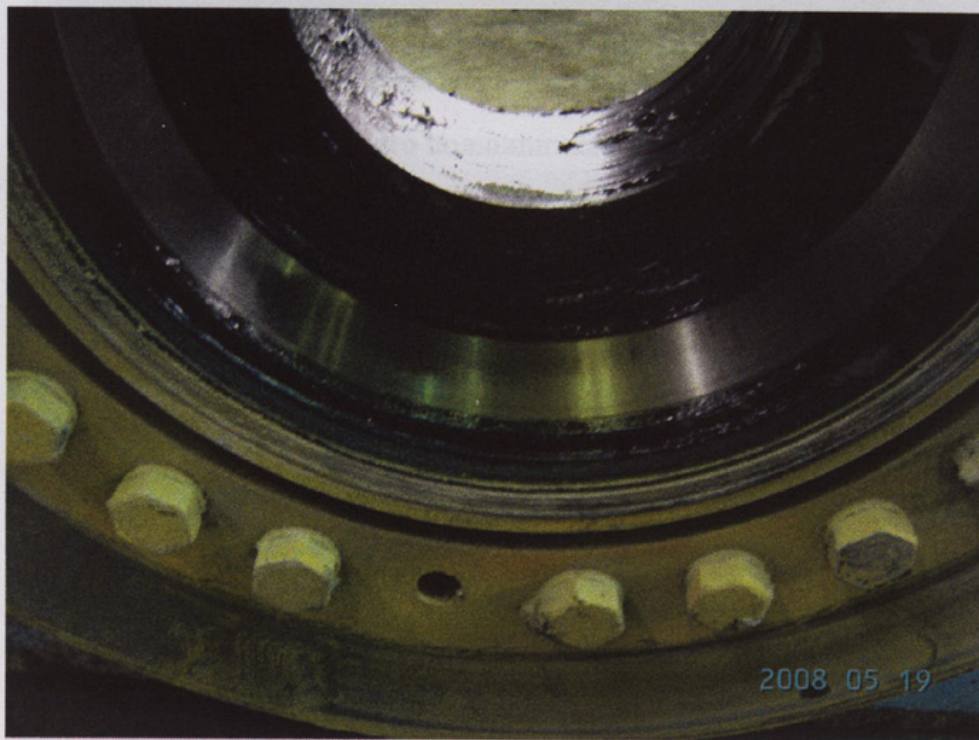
Крышка ступицы со стороны внутреннего кольца подшипника со смазкой МС-1000.
